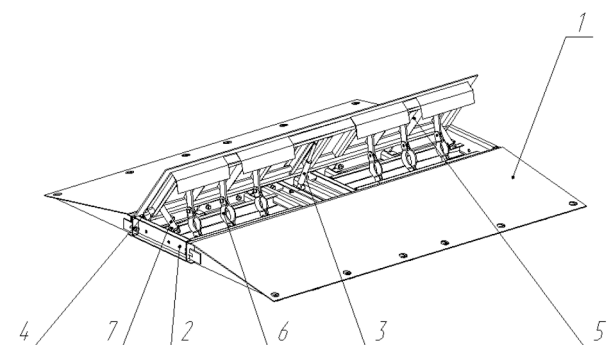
Типовая конструкция дорожного блокиратора с подъемной платформой: 1 — пандус; 2 — рама; 3 — гидравлический привод; 4 — петельное устройство; 5 — подъемная плита; 6 — рычаги; 7 — механизм фиксации
